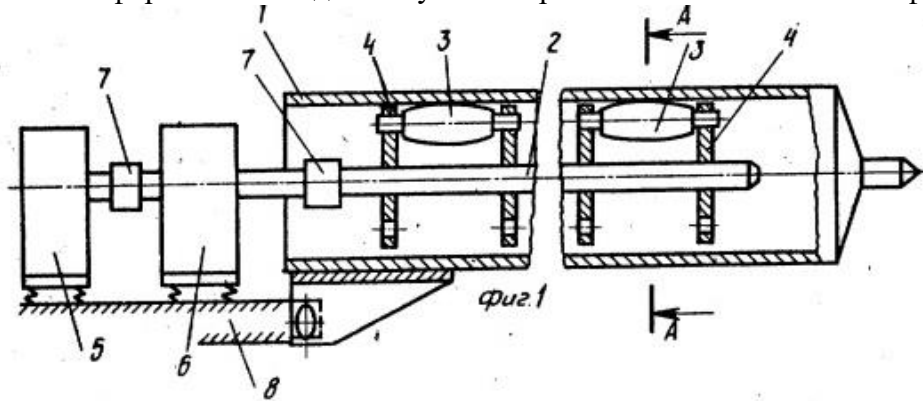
Общий вид: 1- полость корпуса; 2- приводной вал; 3- возбудитель колебаний; 4- диски; 5- двигатель; 6- редуктор; 7- муфты; 8- рама формовочной машины
